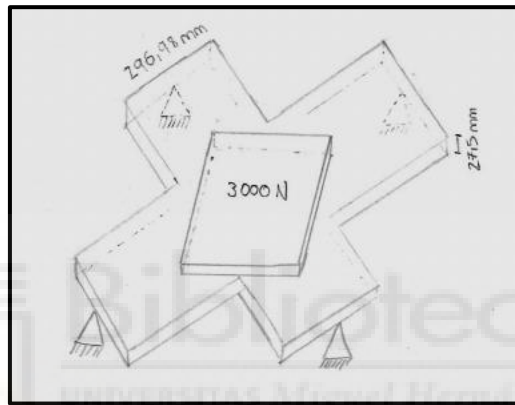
Boceto vigas diagonales con apoyos en las esquinas y fuerza aplicada.
